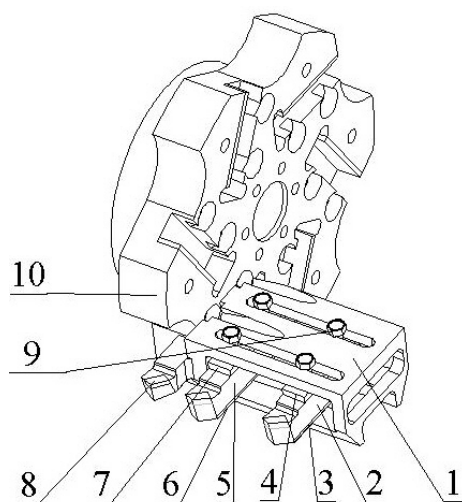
Многорезцовая державка, установленная в револьверной инструментальной головке токарного станка с ЧПУ
